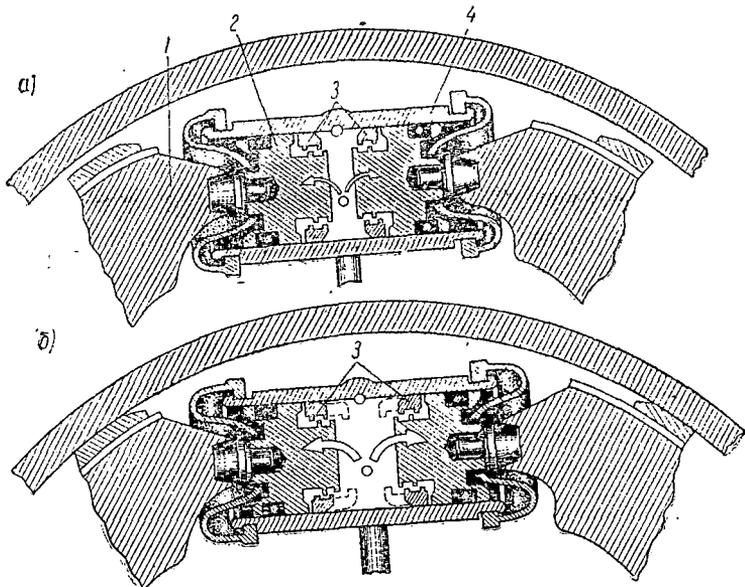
Схема устройства для автоматической регулировки зазора между тормозным барабаном и накладками тормозных колодок:
